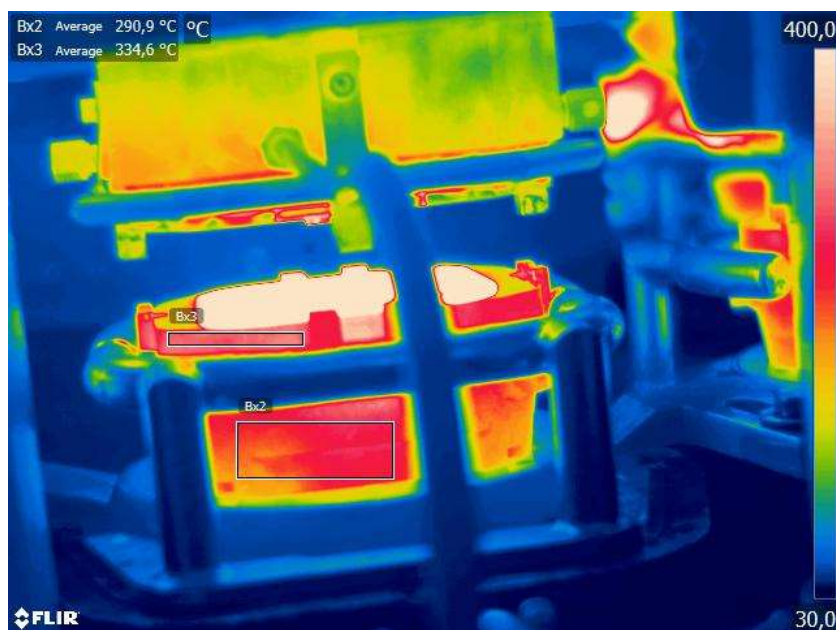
Infračervený snímek formy před dopadem roztavené skloviny, pozice 1
